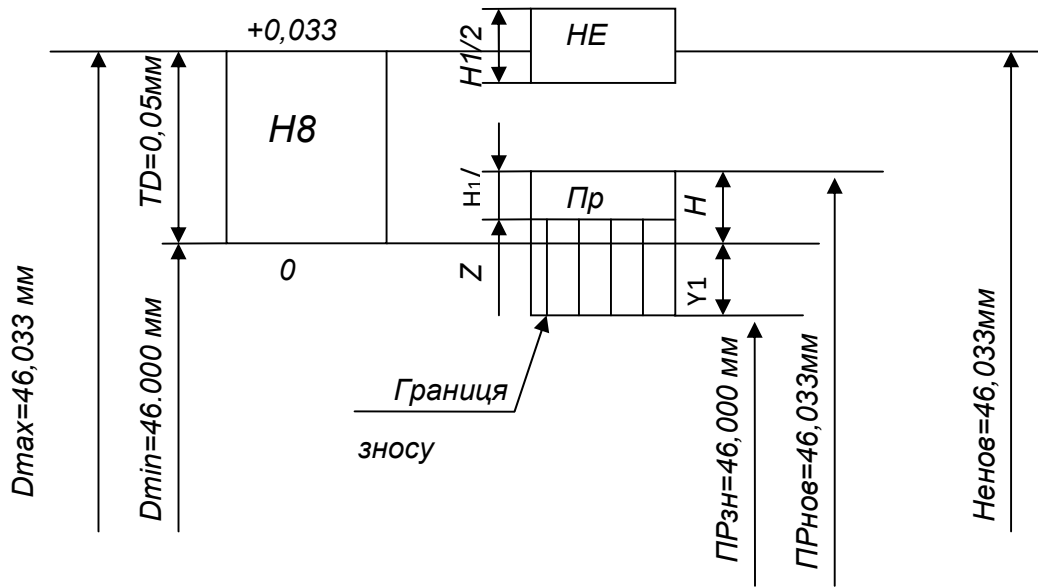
Схема розташування полів допусків калібру–пробки
